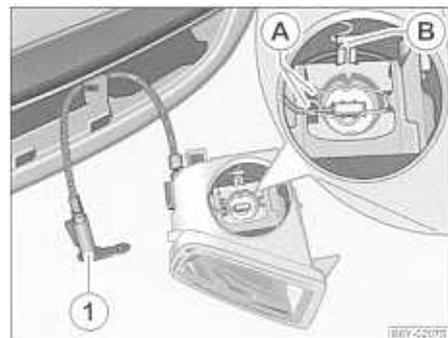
Desmontaje de la bombilla para faro antiniebla
